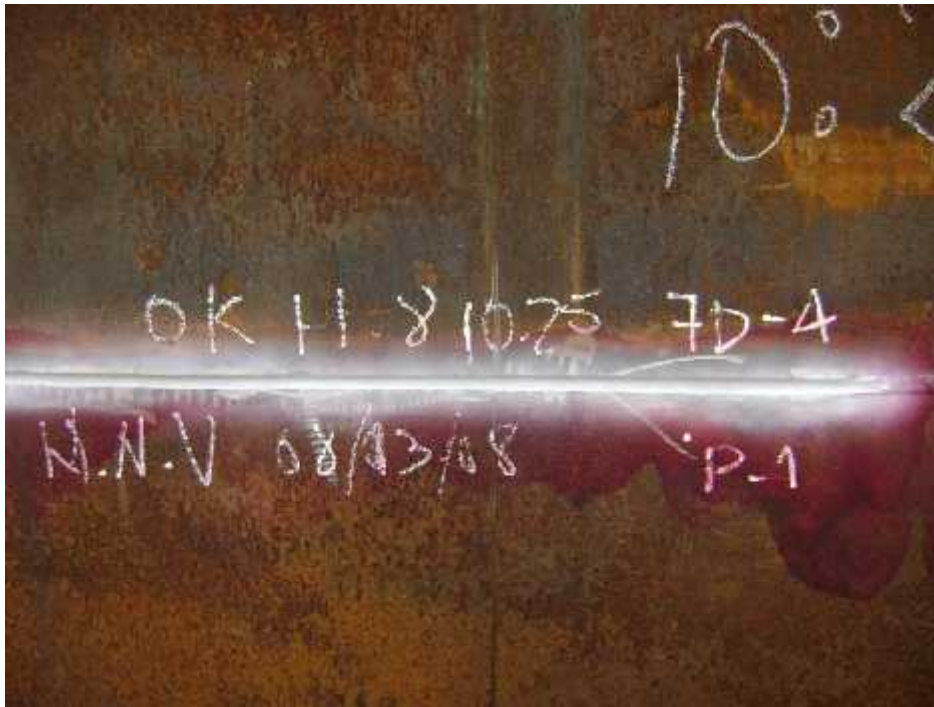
Aplicación de tintes penetrantes en cordon de soldadura (raiz)¹²⁰
